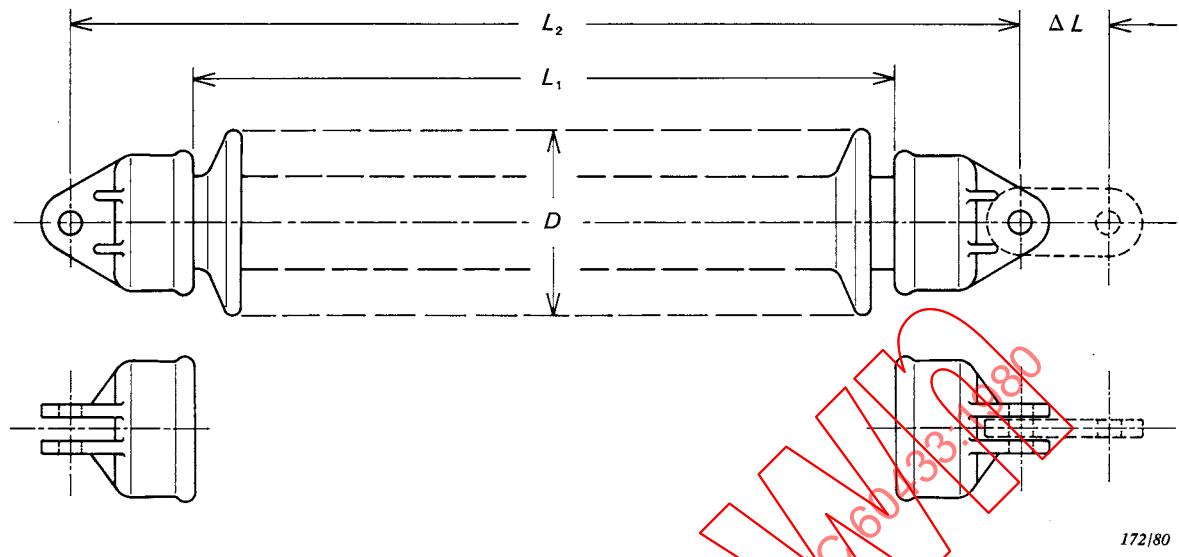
Elément de chaîne avec armatures externes et assemblage à chape et tenon, type CE.
